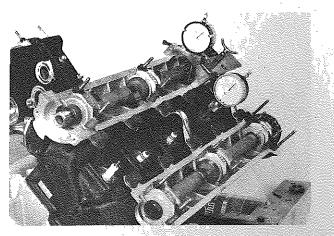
Montare il comparatore n. 42 Fit gauge No. 42
